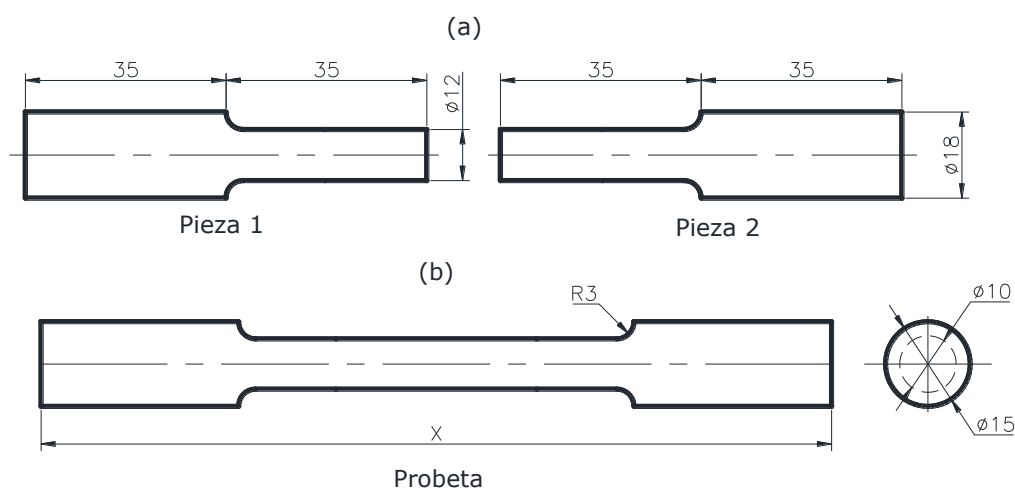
Dimensiones de Piezas y Probeta a) Dimensiones de las piezas para la soldadura. b) Probeta para el ensayo de tracción
